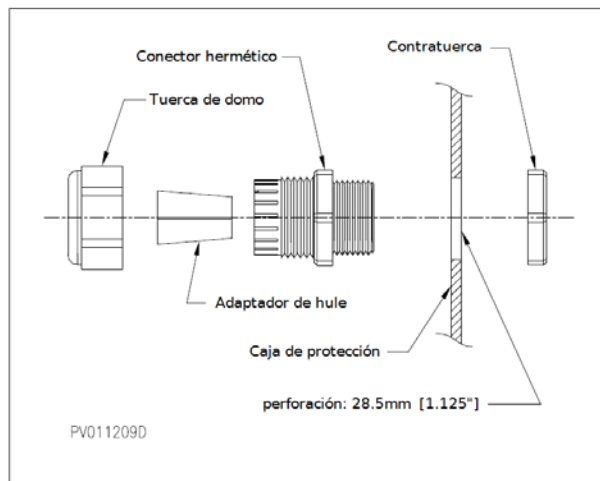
Montaje de los conectores de alivio de tensión a prueba de agua para cable reforzado.
